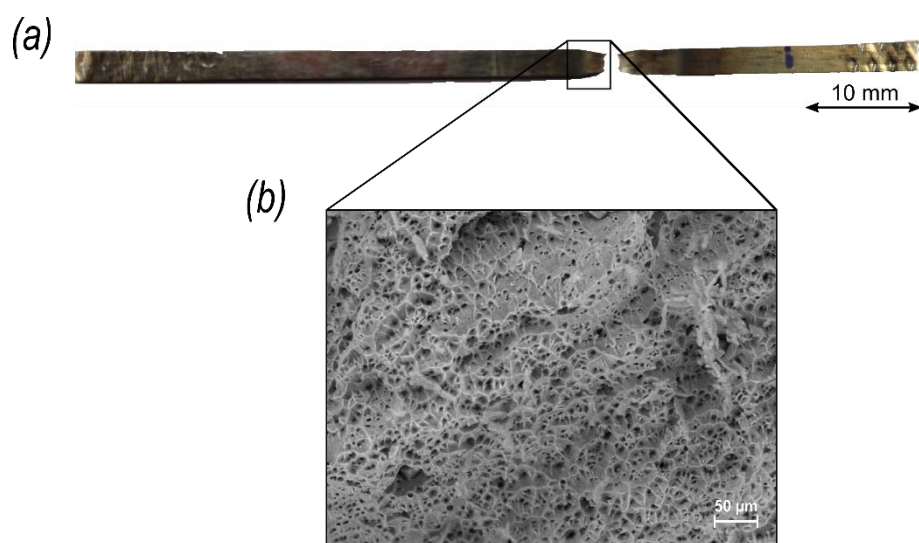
(a) #6_LAE_2 após ensaio de tração uniaxial. (b) Superfície de fratura.
